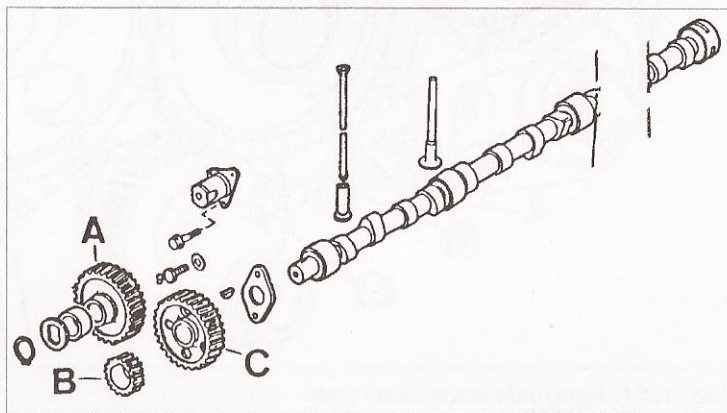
Распределительный вал (4-цилиндровый и 6-цилиндровый двигателя).
